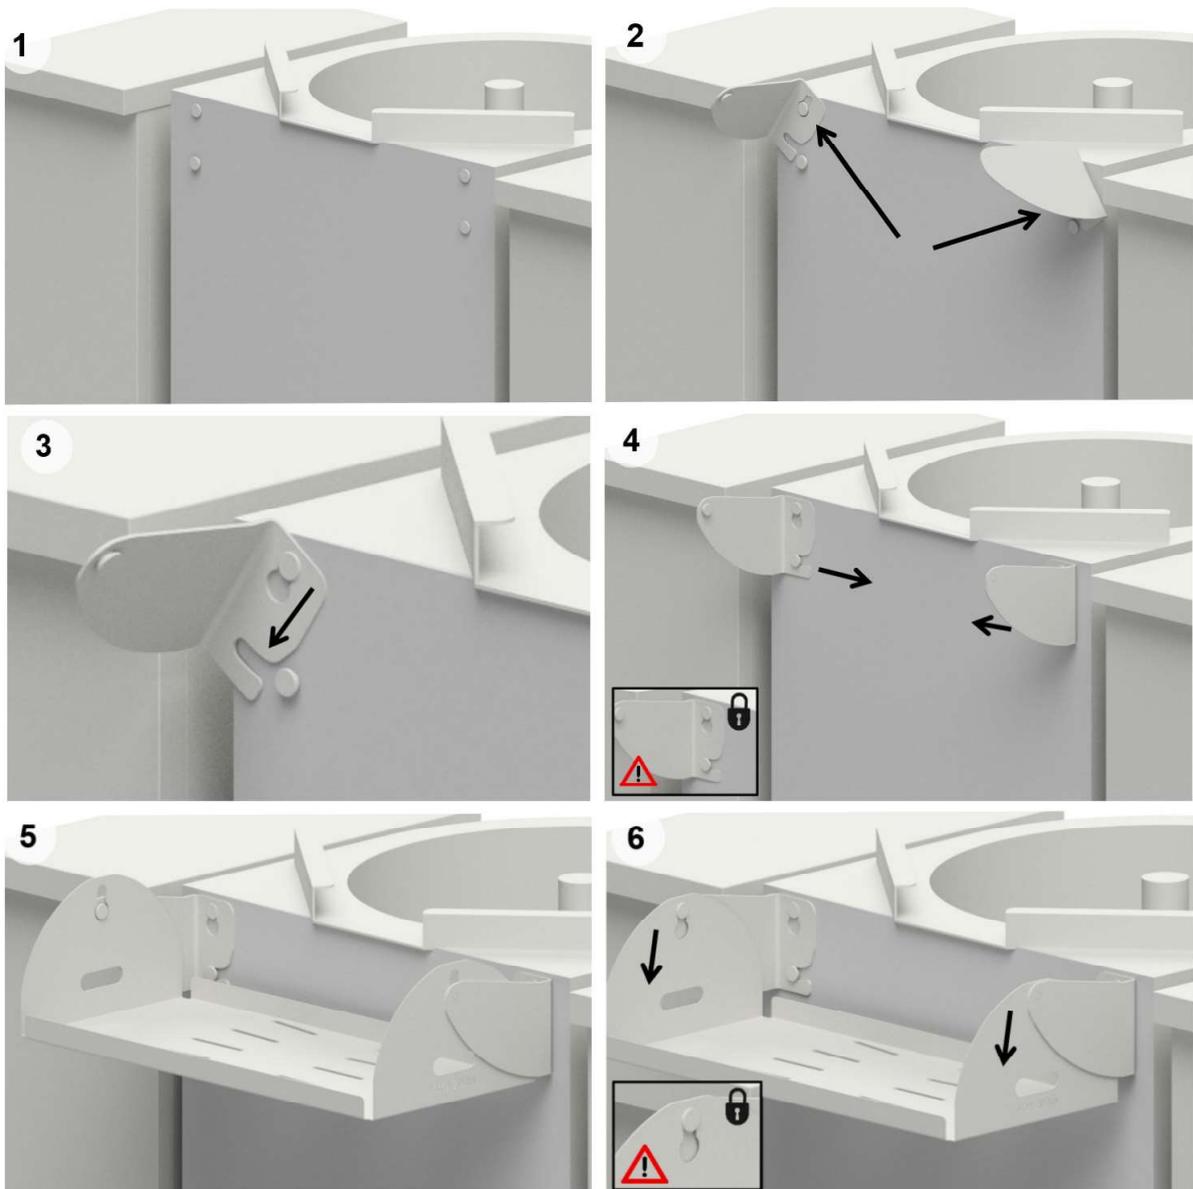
Befestigung der GN-Potionierhilfe an Kessel mit gerader Front
